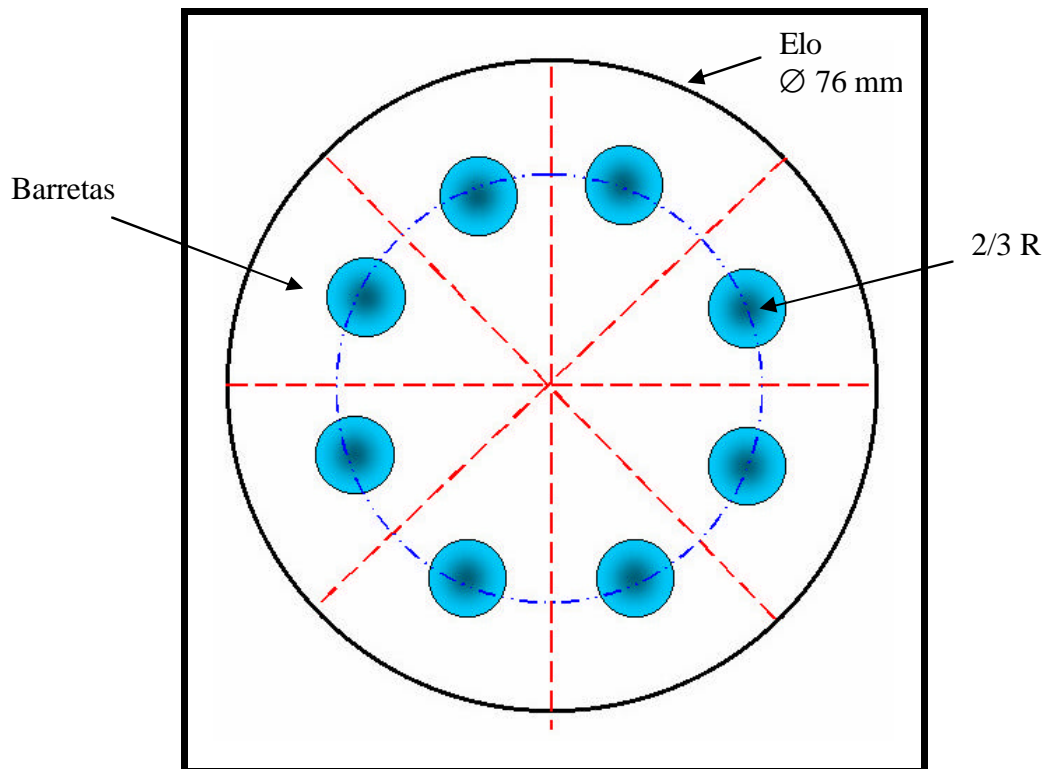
Posição de retira das barretas em função do diâmetro do elo.
